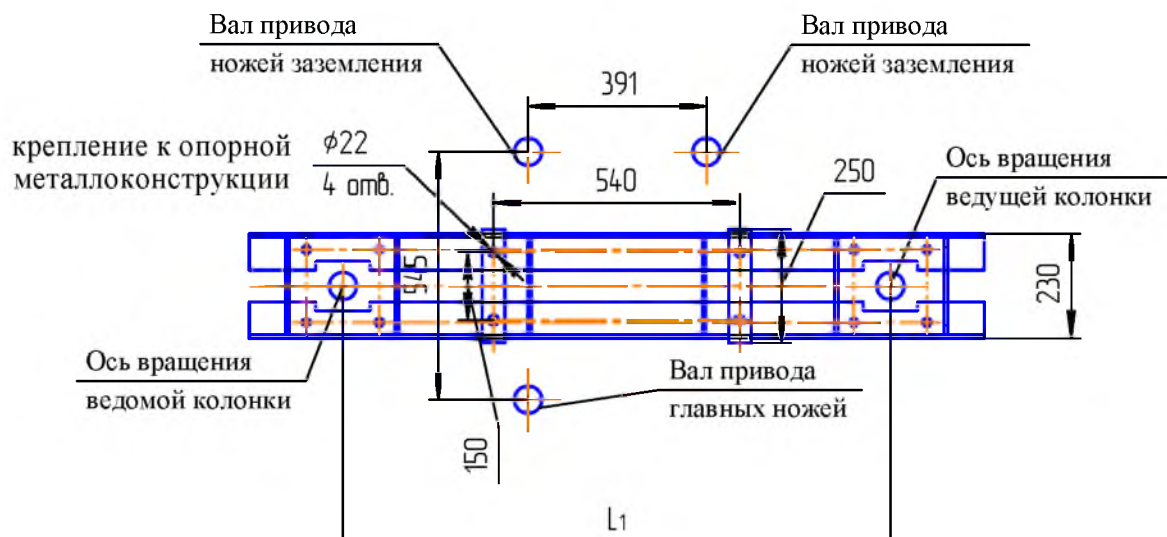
Общий вид трехполюсного разъединителя РН(П) СЭЩ®-110/□
